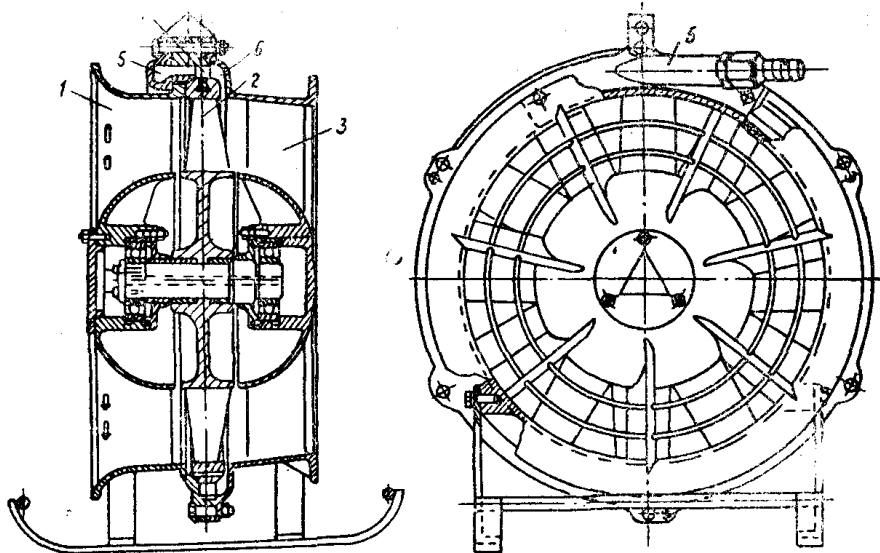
Разрез вентиляторного агрегата типа ВП-4: 1—направляющий аппарат; 2—рабочее колесо вентилятора; 3—спрямляющий аппарат; 4—турбинка; 5—сопло; 6—канал для сброса воздуха, отработавшего в двигателе.
